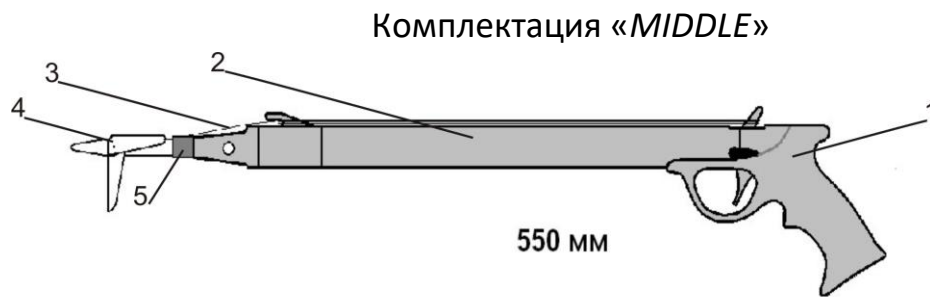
1-рукоятка, 2-ресивер, 3-линь, 4-гарпун, 5-втулка скользящая
